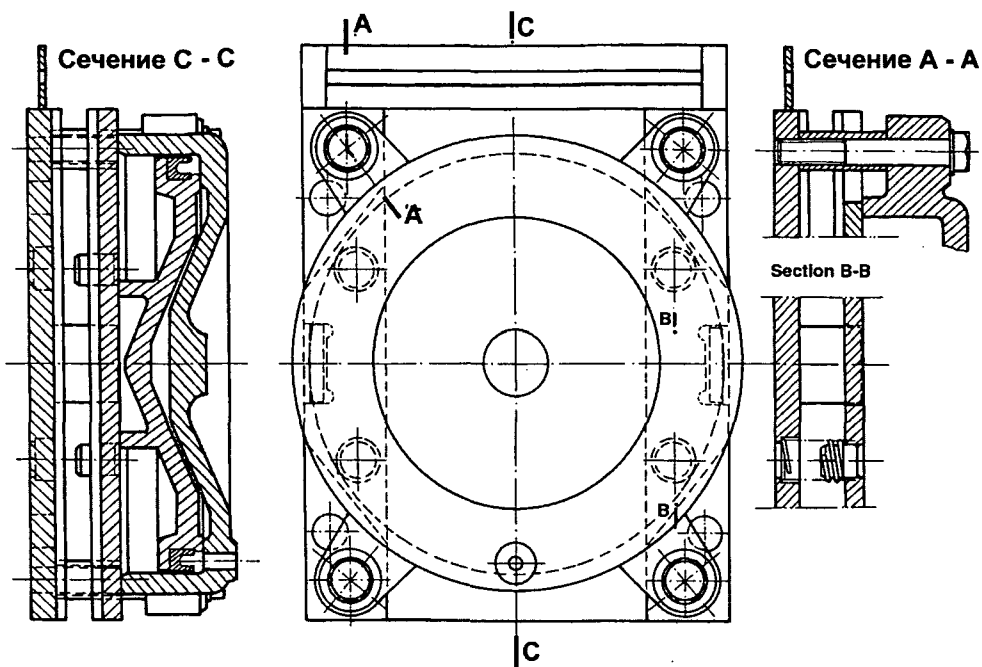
Канатный тормоз (BODE Aufzuge)
